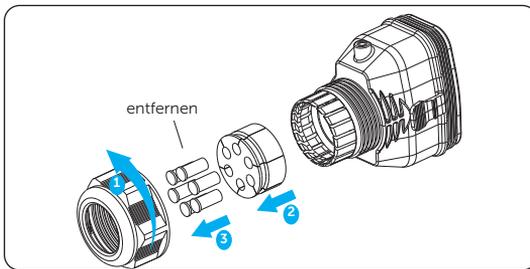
Das Gehäuse des Steckverbinders demontieren
